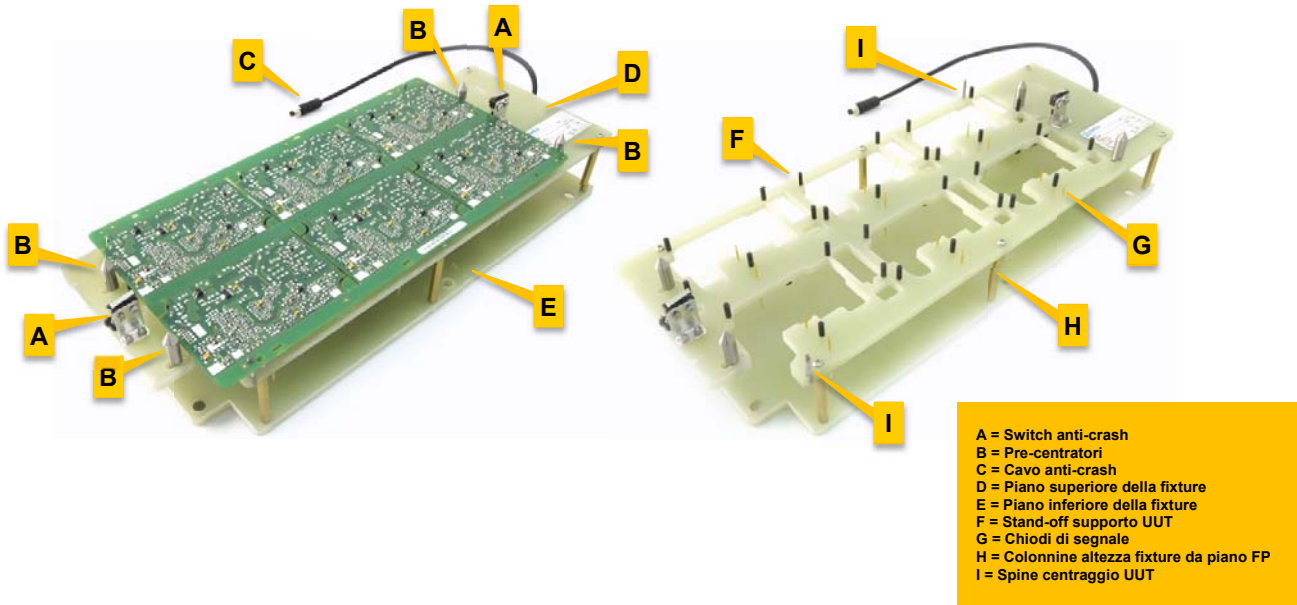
Esempio di fixture per sistema In-Line per pannello a 6 figure.
